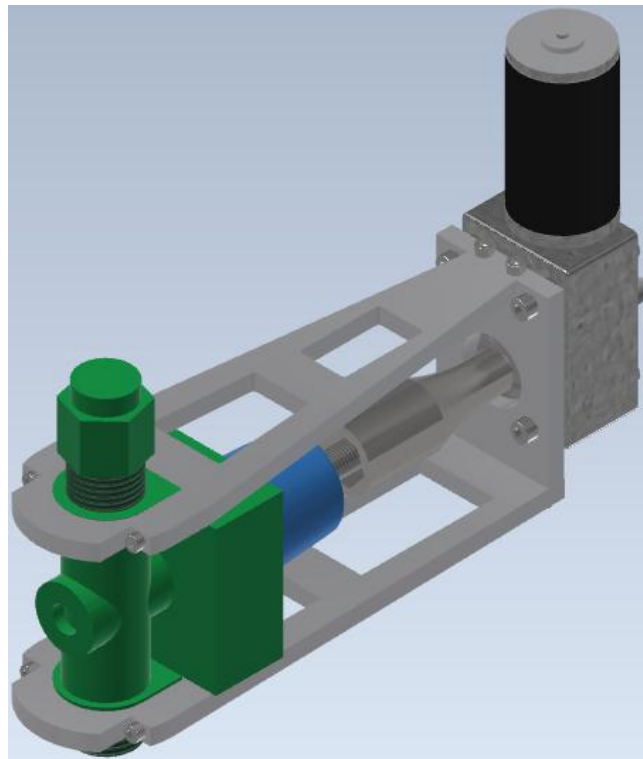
Ensamble de componentes mecánicos en Inventor ®
